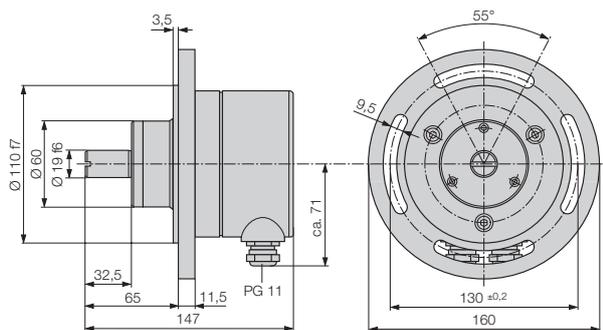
KINAX WT 707 mit Schraubklemmen sowie Stopfbuchsen und Flansch.
